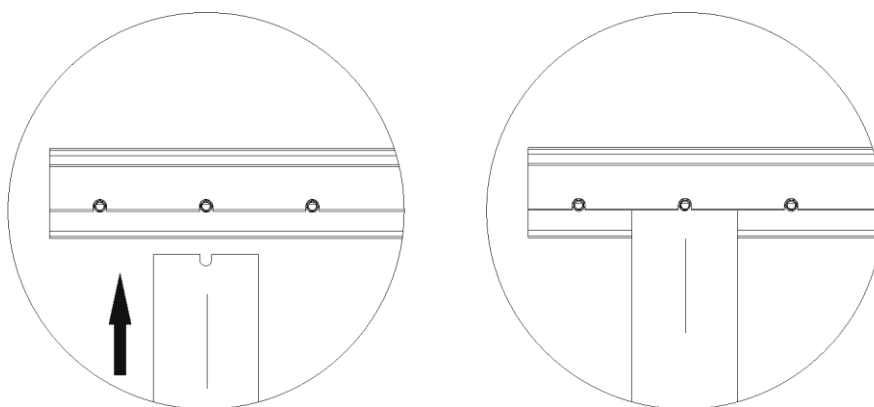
Образец установки соединительной панели, исполнение "моно"
